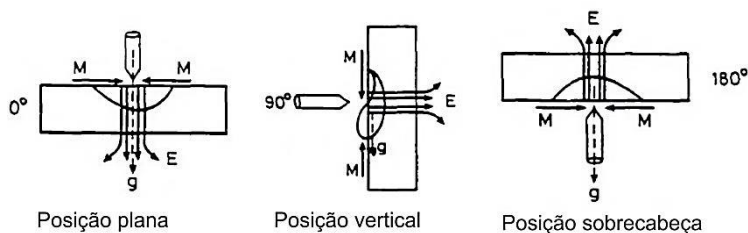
Desenho esquemático representando a influência da posição de soldagem sobre o perfil do cordão de solda, e sobre a força eletromagnética (E), gravitacional (g) e induzida pelo gradiente de tensão superficial (M). Adaptado de [59].
